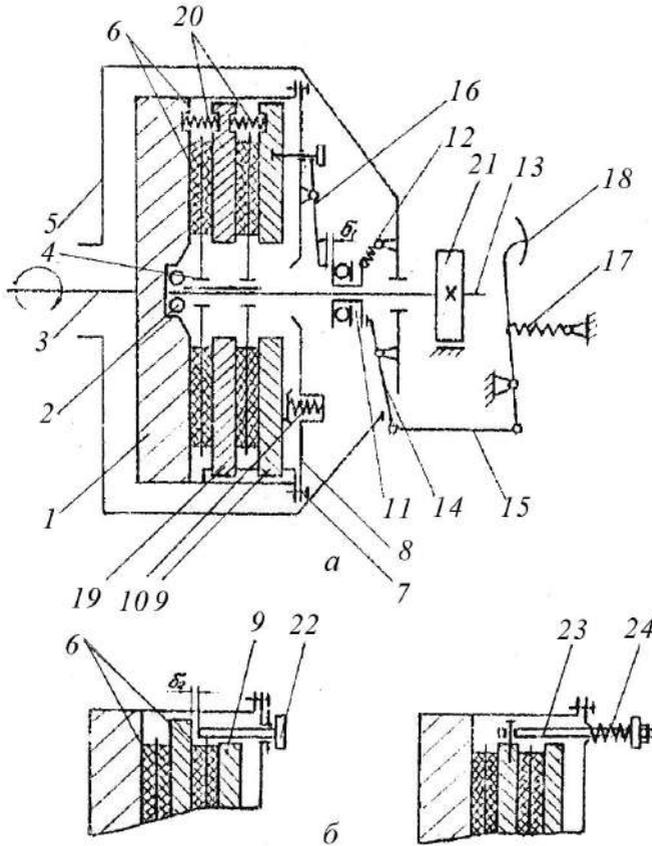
Конструктивна схема зчеплення: *а* – з механізмом розведення дисків пружинами; *б* – механізмами розведення дисків упорами та тягами; 1 – маховик; 2 – підшипник; 3 – колінчастий вал; 4 – маточина; 5 – картер; 6 – ведений диск у зборі; 7 – болти; 8 – кожух; 9 – натискний диск; 10 – натискні пружини; 11 – підшипник вимкнення; 12 – відтяжна пружина; 13 – вал зчеплення; 14 – вилка вимикання; 15 – тяга; 16 – важелі вимикання; 17 – поворотна пружина; 18 – педаль; 19 – проміжний диск; 20 – пружні розводки; 21 – гальмо; 22 – упорний гвинт; 23 – тяга; 24 – відтяжна пружина
